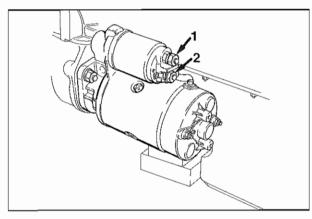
Cavi motorino d'avviamento (C. mec.) Starter motor cables (Gearbox)
